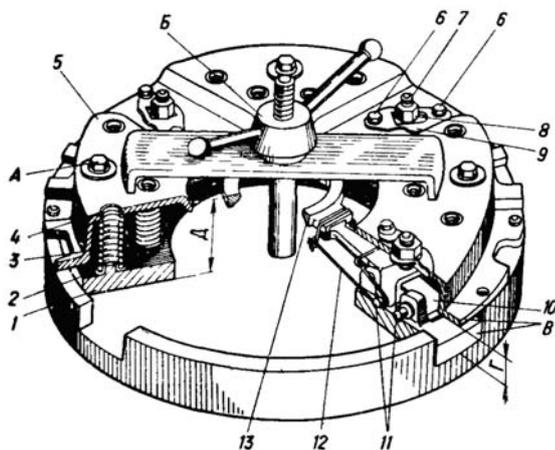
Разборка кожуха: 1 — диск нажимной; 2, 4 — стакан; 3, 12 — пружина; 5 — кожух; 6 — болт; 7 — вилка; 8 — гайка; 9 — пластина; 10 — рычаг; 11 — ось; 13 — кольцо упорное; А — болт технологический; Б — приспособление; В — метка; Г, Д — размер
